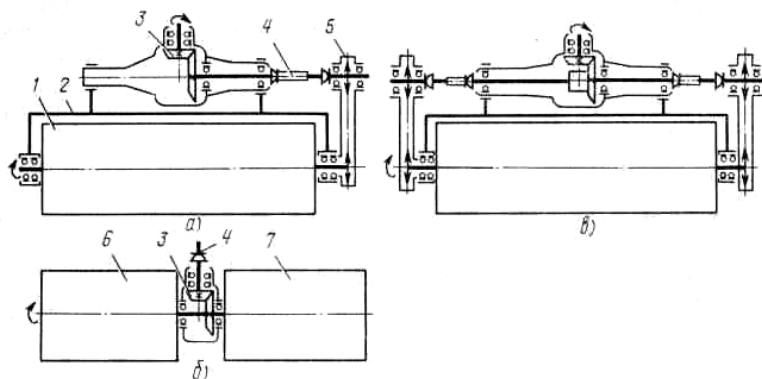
Схемы приводов рабочего органа фрезы: а – односторонний боковой; б – двусторонний боковой; в – центральный:
